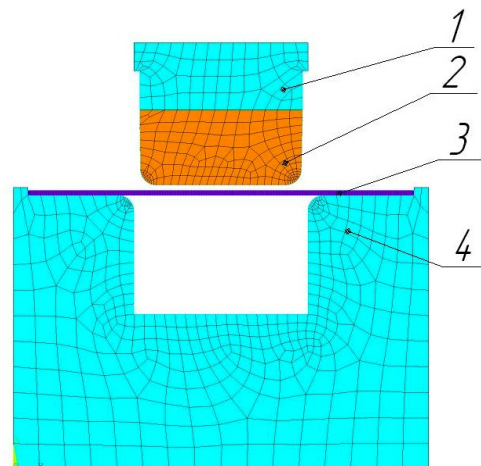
Конечно-элементная модель: 1 - корпус; 2 - полиуретановый пуансон; 3 - заготовка; 4 - матрица
